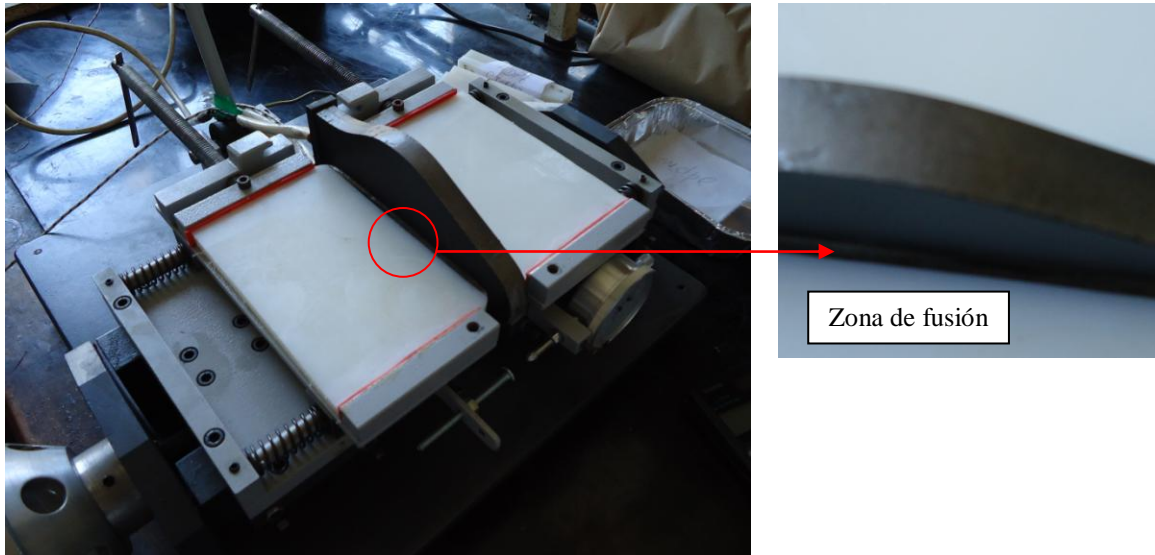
Calentamiento y fusión de las placas a soldar.
